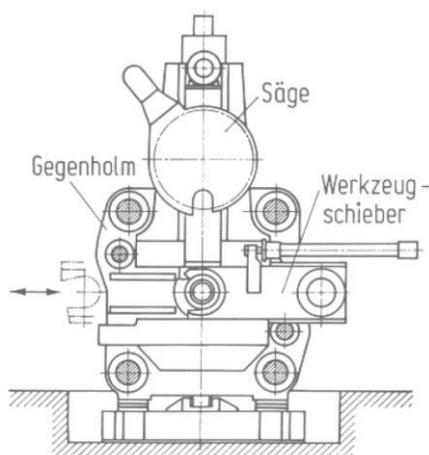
Werkzeugschieber<sup>(Lange, S. 442)</sup>
